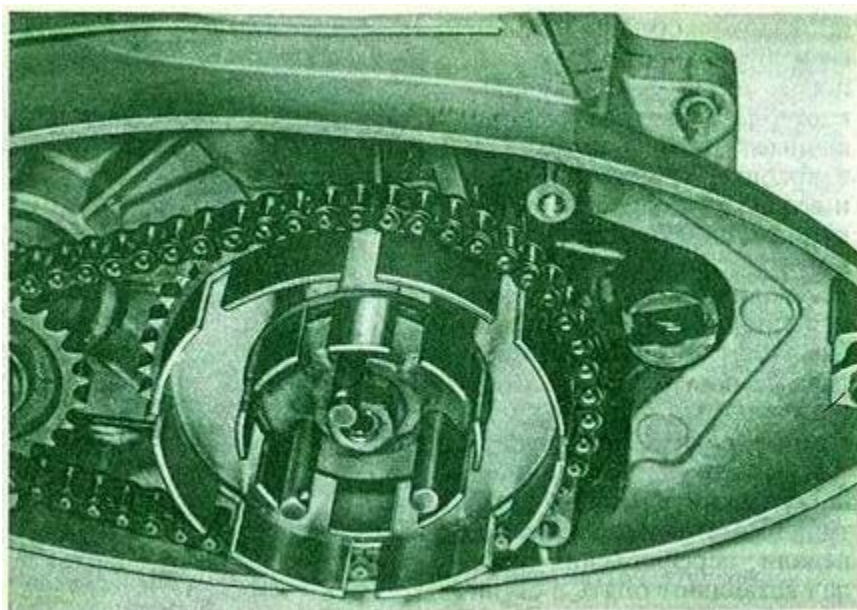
Ведущий и ведомый барабаны сцепления старой конструкции
